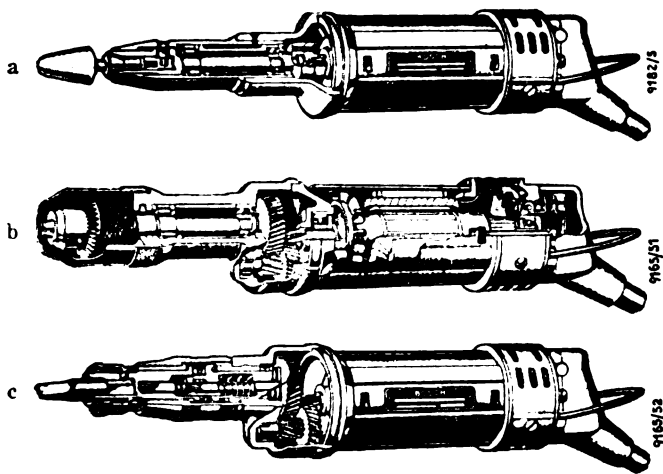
Schnelllaufender Handschleifer a, Handmotor b und Schrauber c der 100 W-Allstromrelhe.
